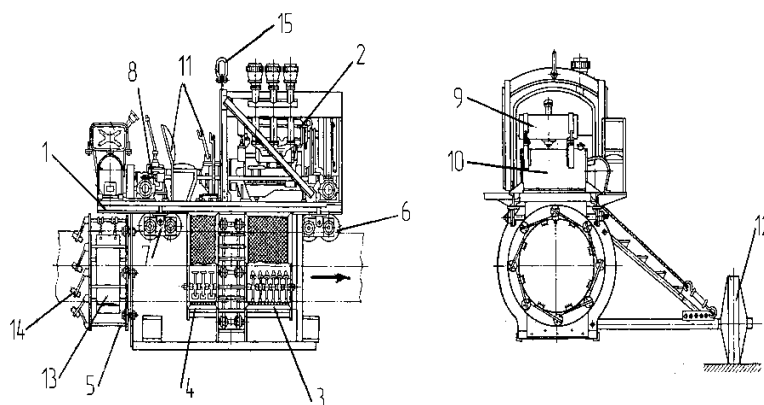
Самоходная очистная машина для трубопроводов: 1 - несущая рама; 2 - силовая установка; 3 - скребковый рабочий орган; 4 - щеточный рабочий орган; 5 - ротор праймирования; 6,7 - опорные колеса; 8 - коробка перемены передач (КПП); 9 - топливный бак; 10 - бак для грунтовки; 11 - сиденье машиниста и органы управления; 12 - дополнительное колесное устройство; 13 - джута-кордовые полотенца; 14 - щетки с мягким ворсом; 15 - грузовая подвеска
